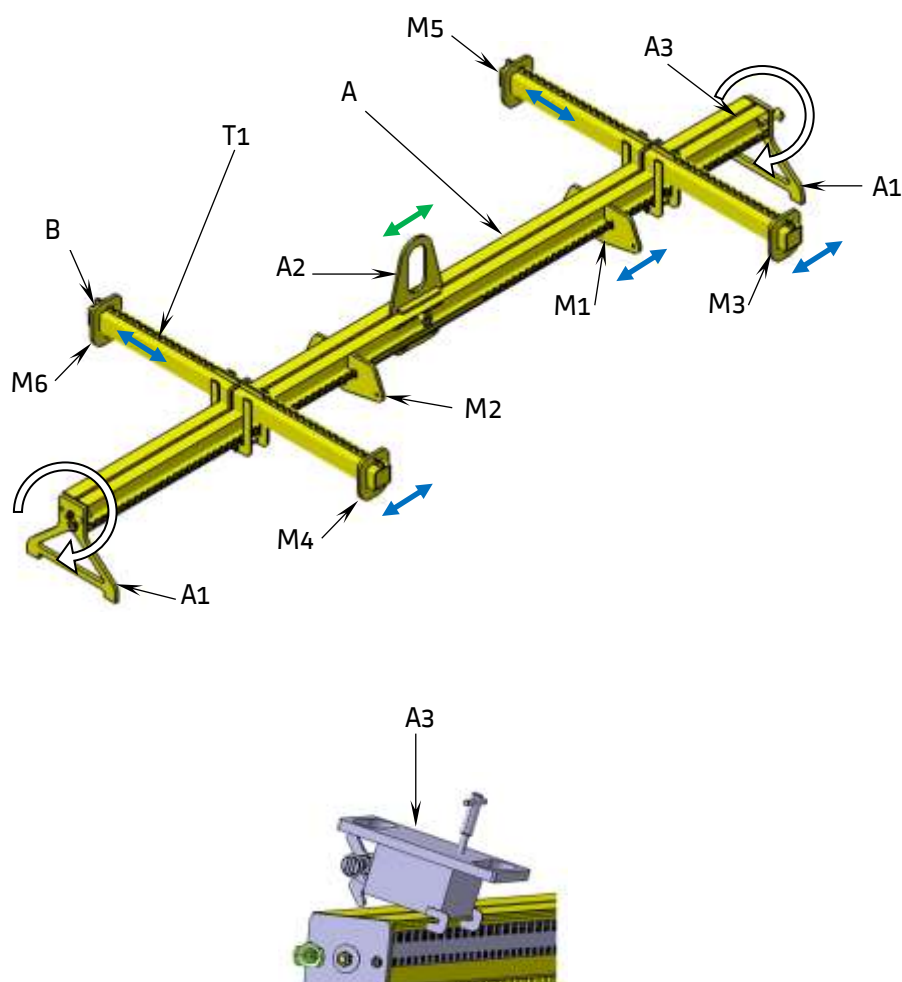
BARRA DE ELEVAÇÃO PARA APARELHOS EM TETOS
